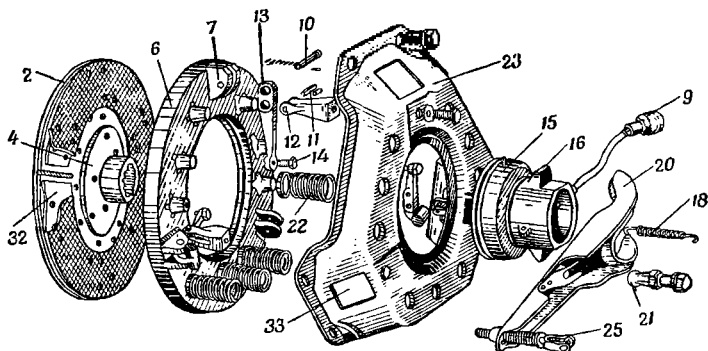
Детали однодискового сцепления автомобиля ГАЗ-51.
